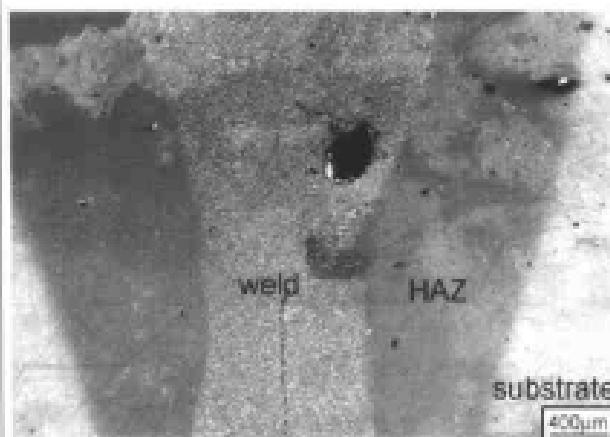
激光焊接, 42CrMo 合金/42CrMo 合金, CO<sub>2</sub> 激光, 焊缝, 功率 3200W, 焊接速度 2m/min.
